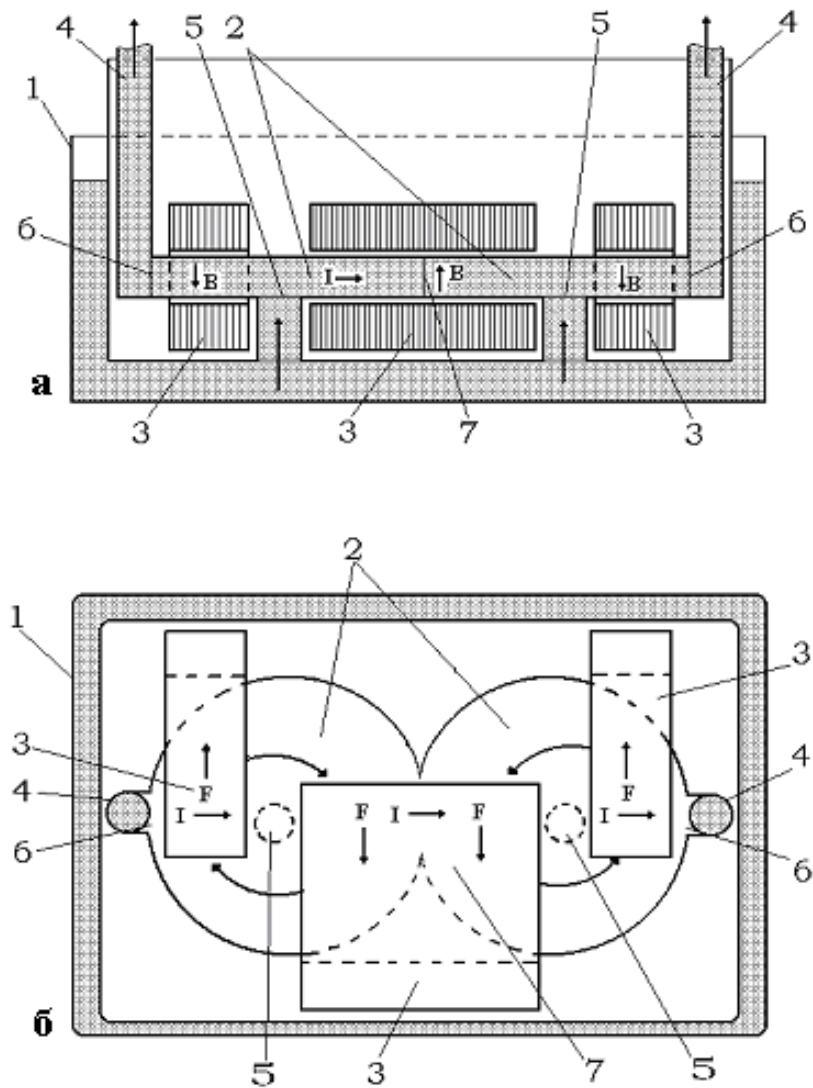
Устройство электромагнитной разливки металла: а) вид сбоку (разрез), б) вид сверху.
